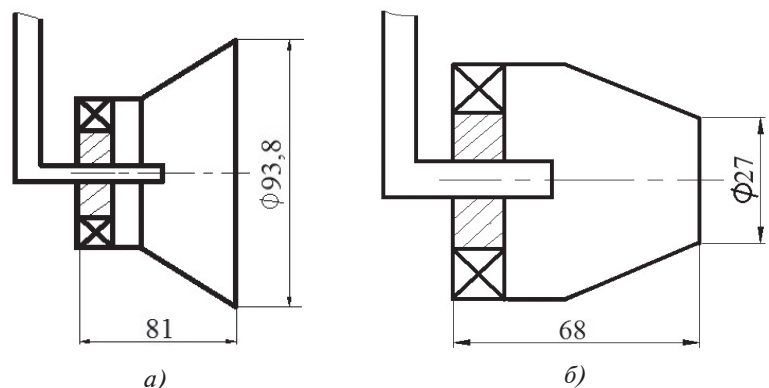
Конструкция горелки: а — горелка №1; б — горелка №2
